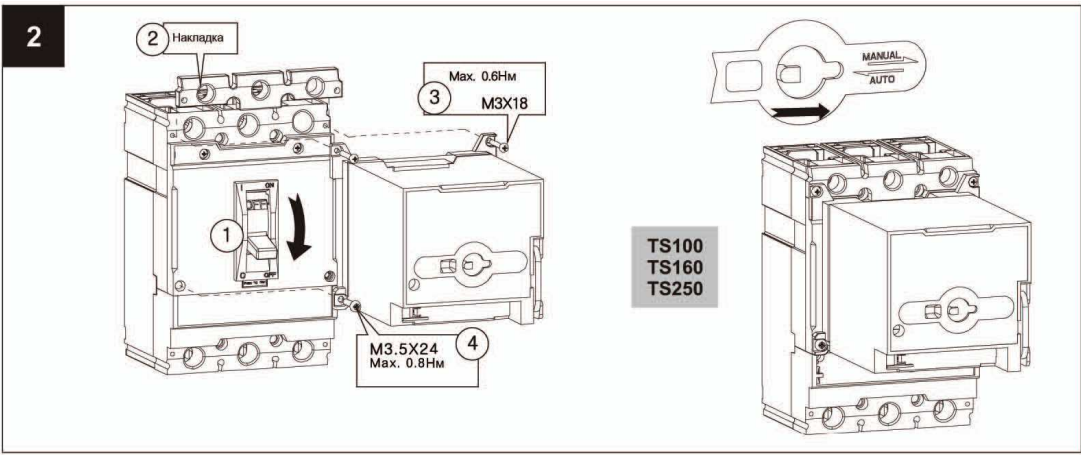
Установка моторного привода на выключатели TS100-TS250
